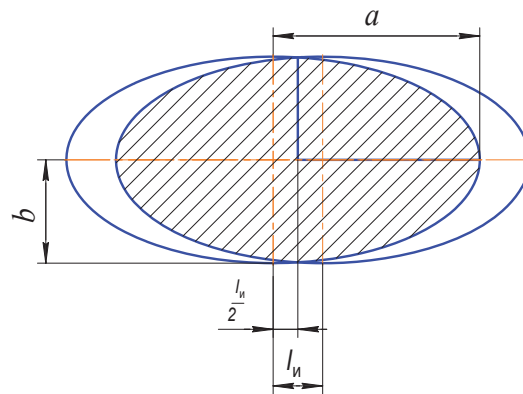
Геометрические параметры сварочной точки эллиптической формы
